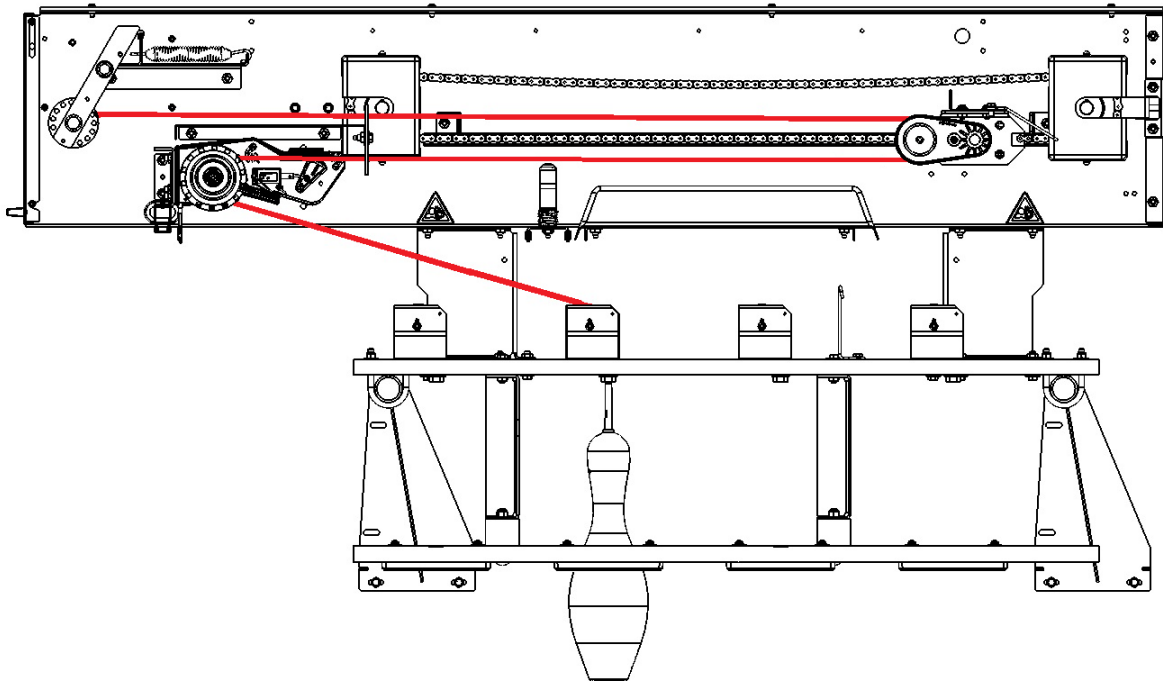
, Parcours corde (quille 5 indiquée en rouge)
